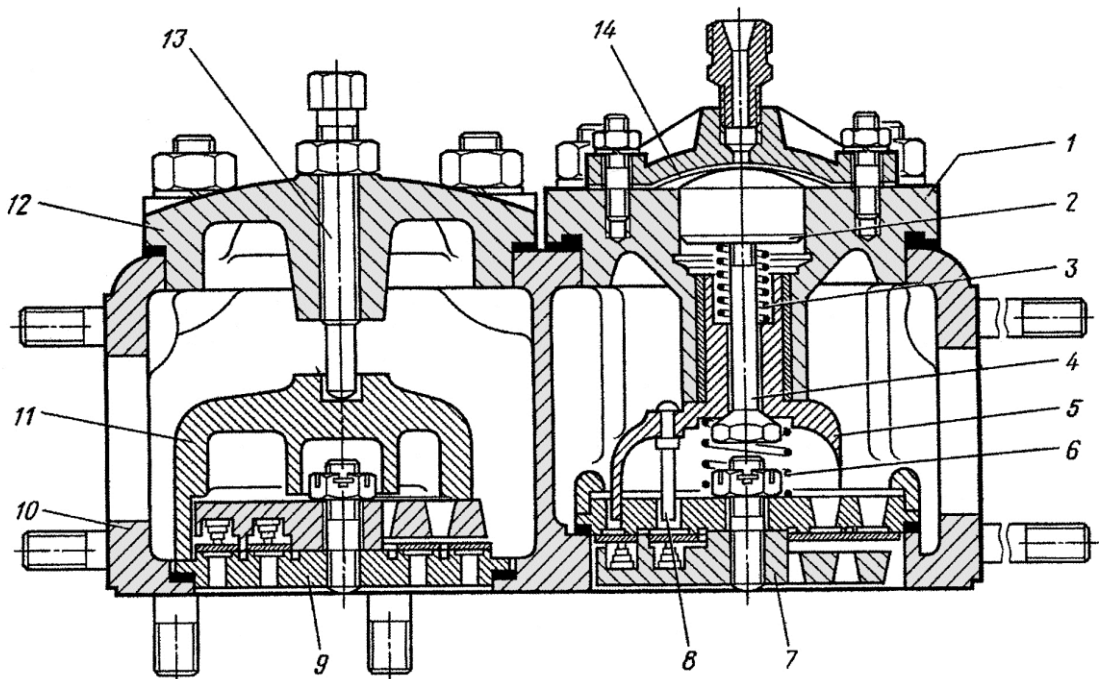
Клапанная коробка первой ступени сжатия компрессора
